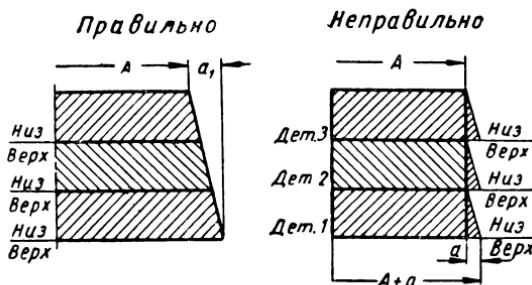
Соединение нескольких деталей, образующих общую поверхность
